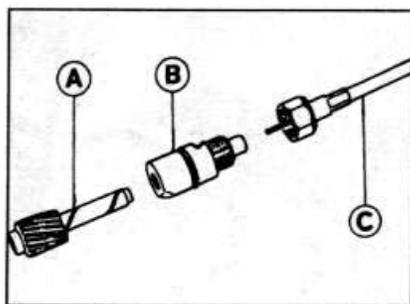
А.15. Шестерня привода спидометра (А), подшипник шестерни (В) и трос спидометра (С).
